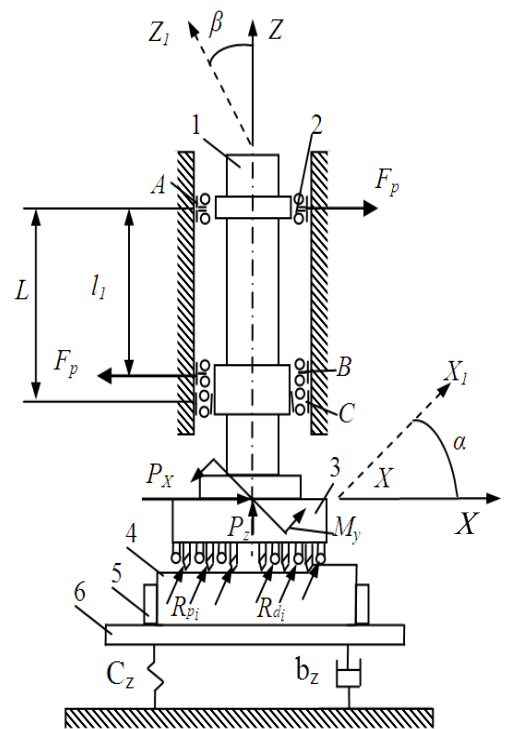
Схема досліджуваної технологічної системи (1 – шпindelь; 2 – підшипникові опори; 3 – інструмент; 4 – заготовка; 5 – пристосування; 6 – стіл)
